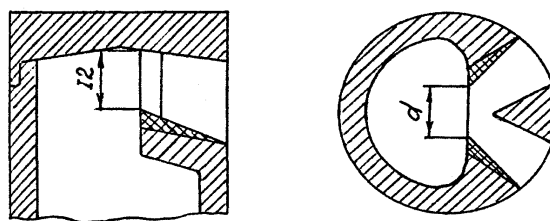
Вертикальный и поперечный профили колпачка с двумя отверстиями
